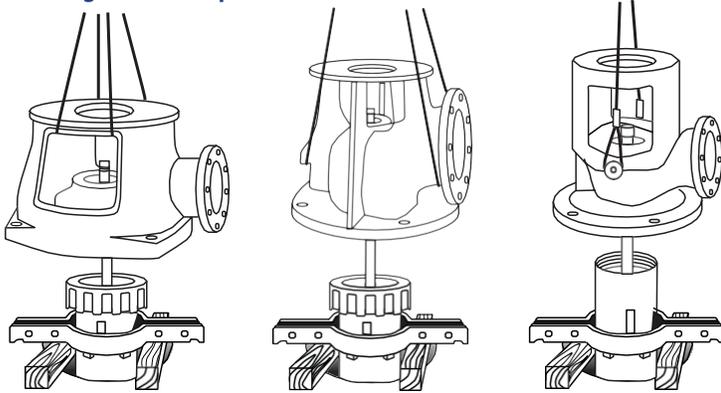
Montaje de la tubería del cabezal a la tubería de la columna
